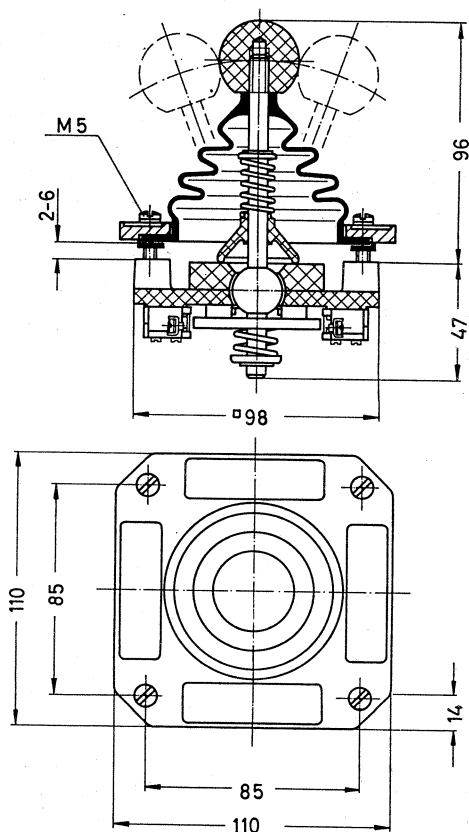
Universal-Steuerschalter, 1-stufige Ausführung,
